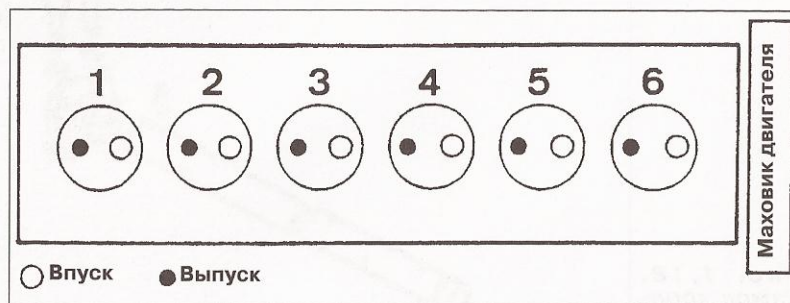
Нумерация цилиндров и расположение клапанов (6-цилиндровый двигатель)
